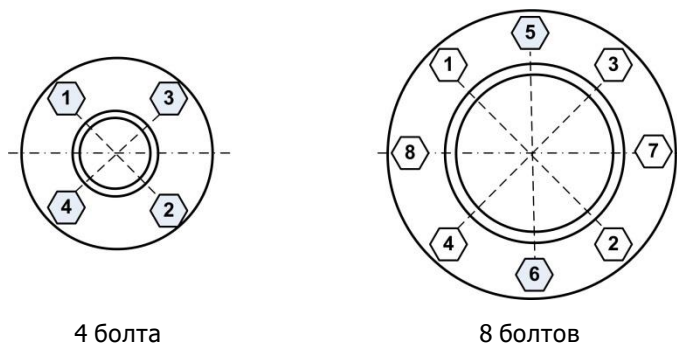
Порядок затяжки или ослабления болтов крепления фланцев
